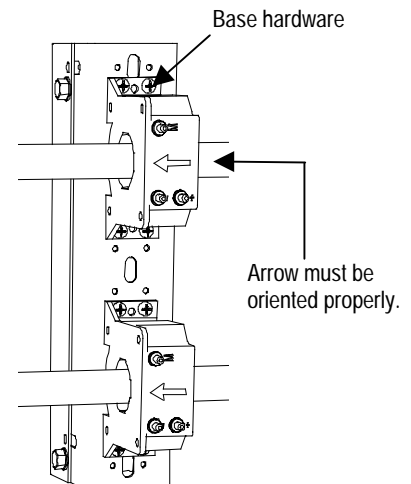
Hall Effekt Position im Schaltschrank mit Detail
